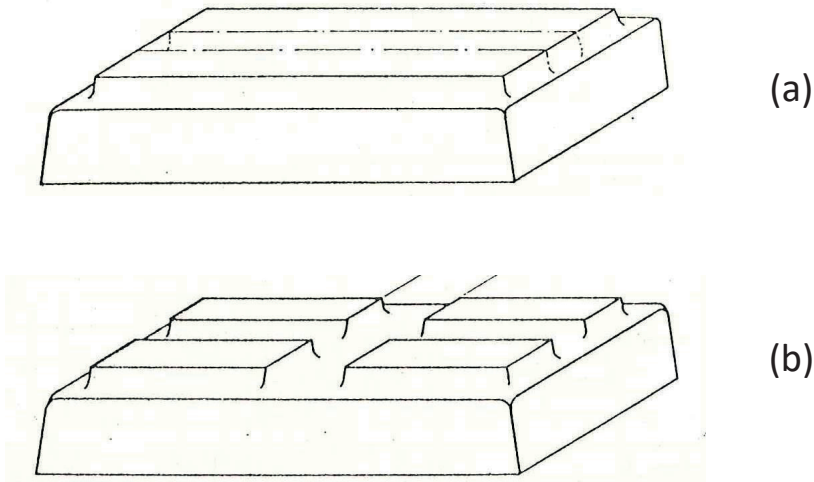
Layout de faces usinadas em base de assento de peças
